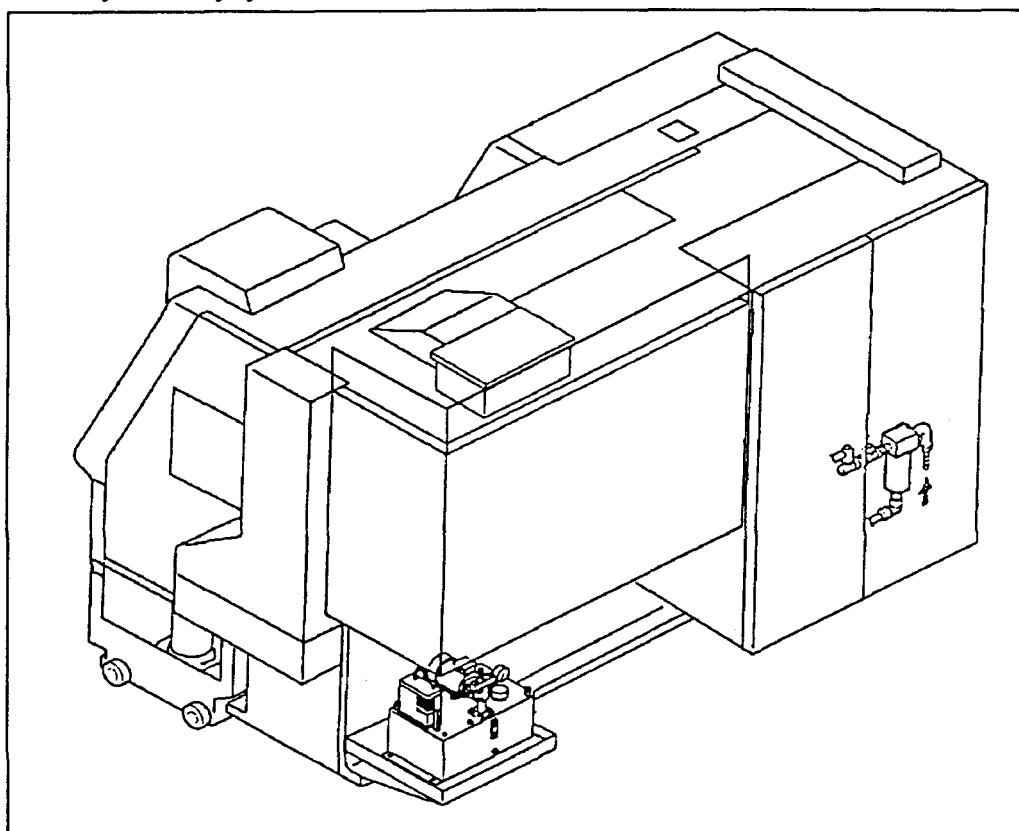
Przyłączenie kabla sieciowego (4/4)
